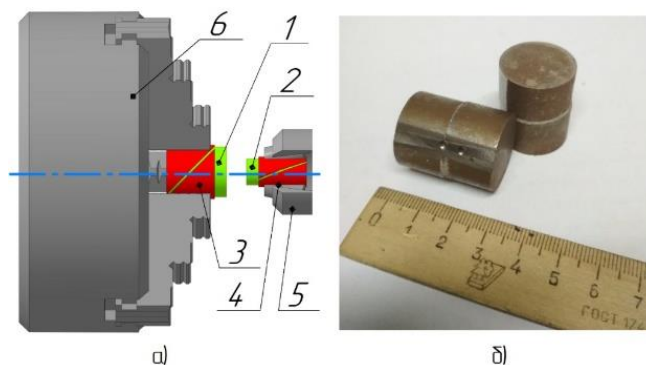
Опытная оснастка (а), сваренные образцы (б) 1 – вращающаяся заготовка, 2 – неподвижная заготовка, 3 и 4 – разрезные обоймы, 5 - сверлильный патрон, закрепленный в задней бабке, 6- трехкулачковый патрон
